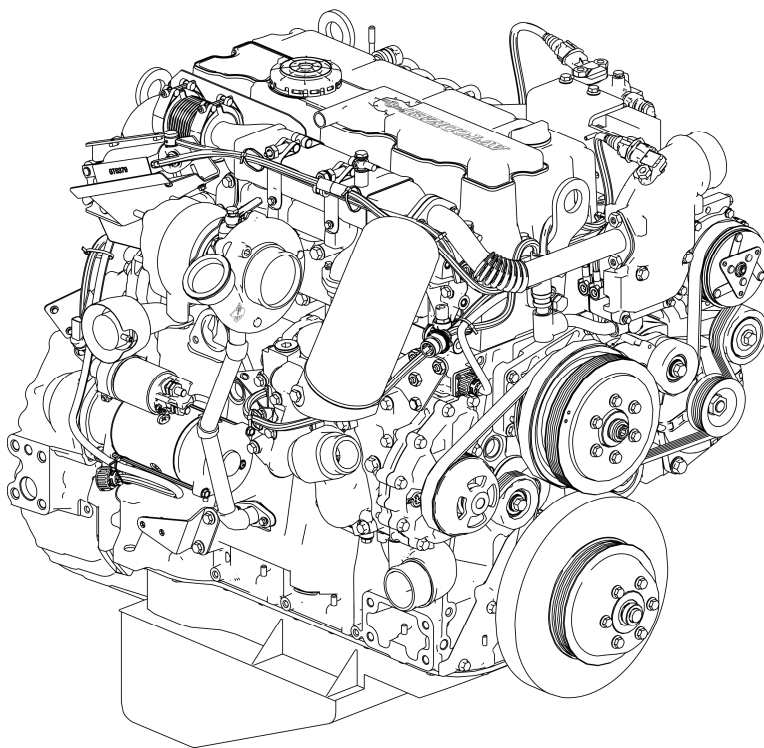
Двигатель ЯМЗ-53472-10 – общий вид справа
